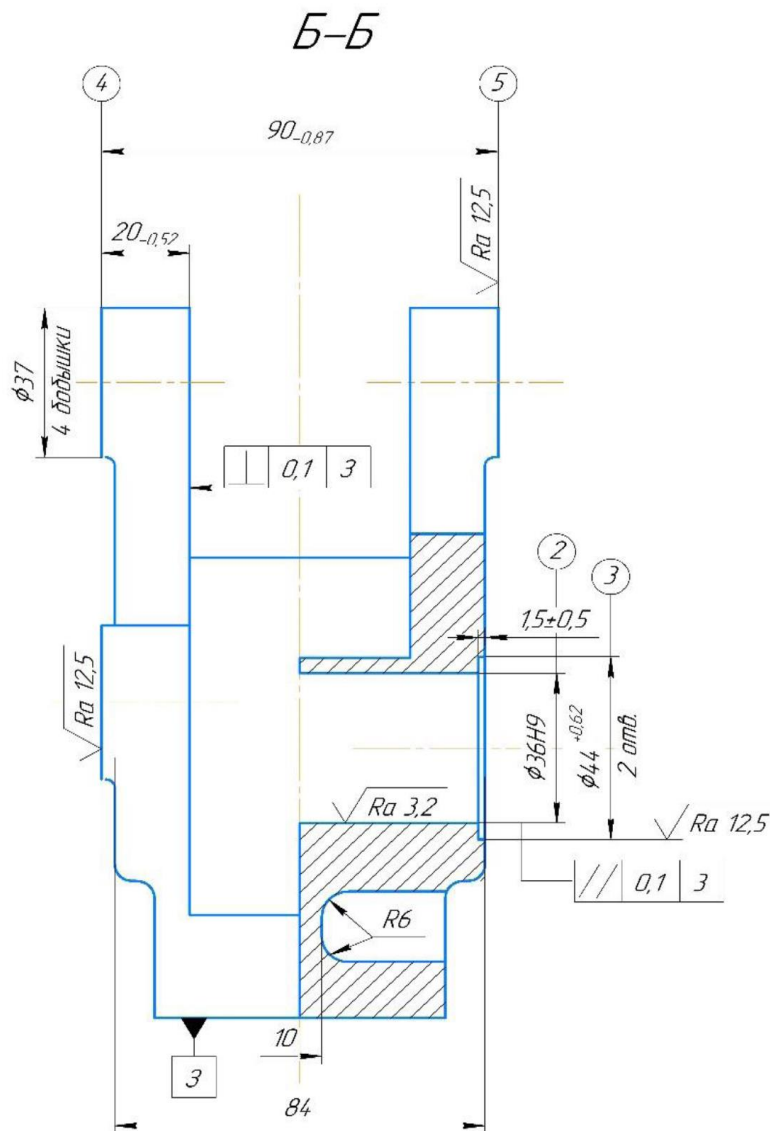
Креслення деталі з нумерацією оброблюваних поверхонь
